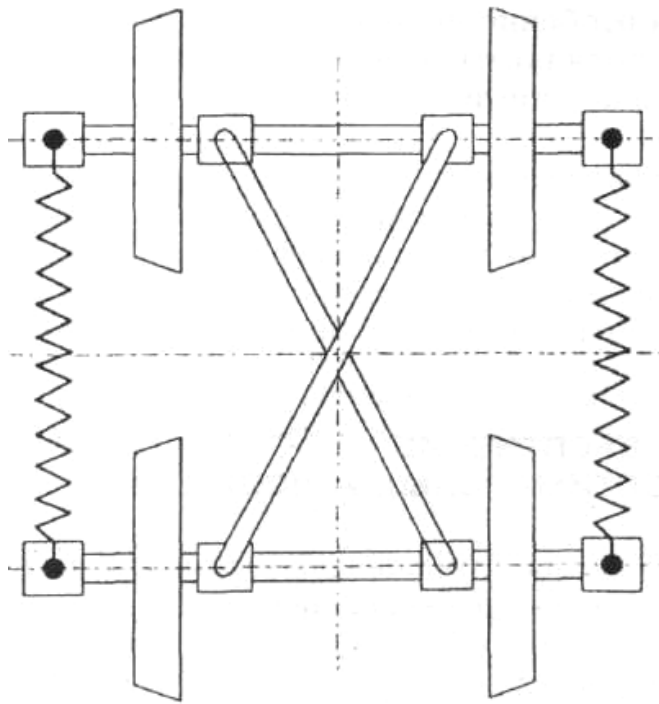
Схема тележки с перекрестными анкерными связями.
